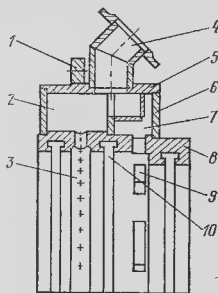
Верхняя часть корпуса концевых уплотнений ЦНД:
